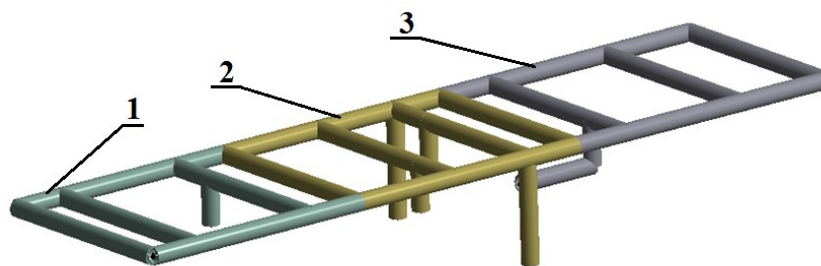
CAD model prototypu křesla při různých konfiguracích II
